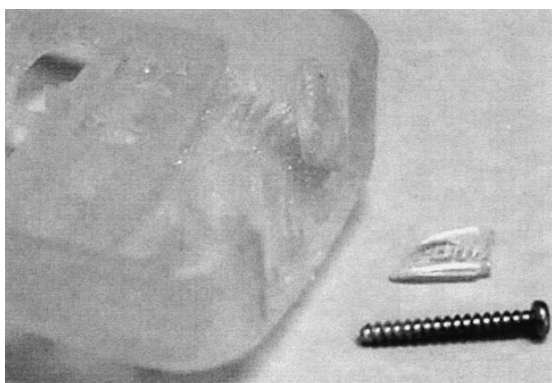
Torre de parafuso quebrada durante os testes de montagem
